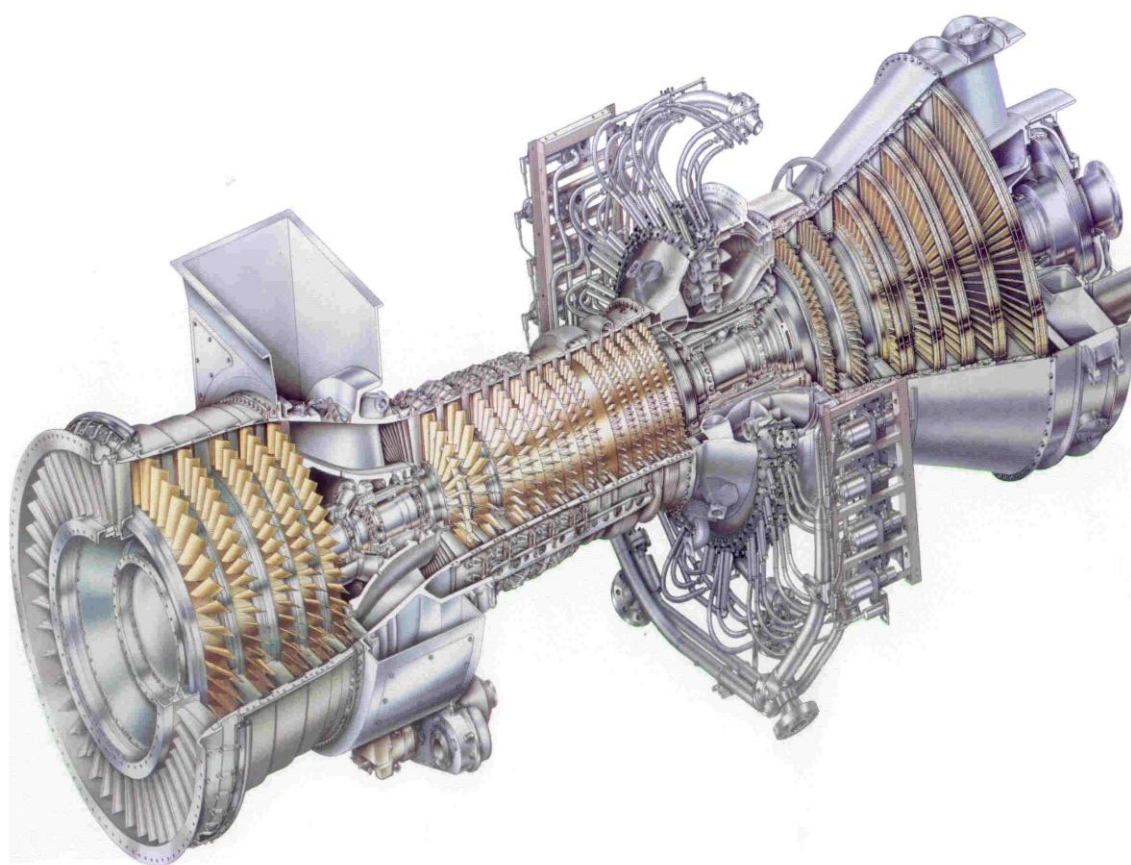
Turbina de Gas (Compresores, turbinas, cámara de combustión).
